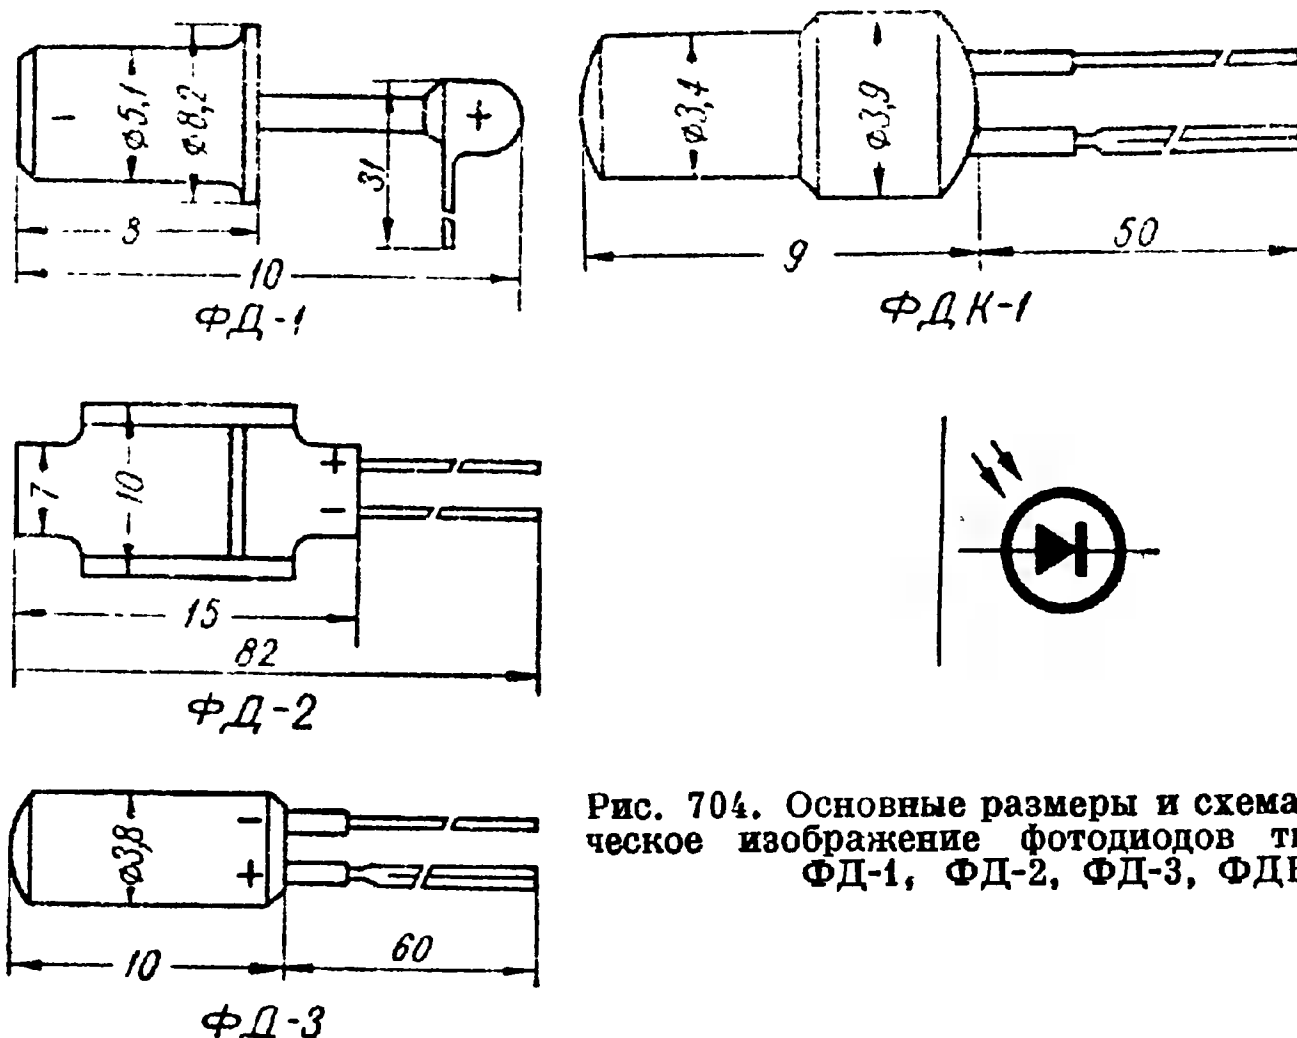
Основные размеры и схематическое изображение фотодиодов типа ФД-1, ФД-2, ФД-3, ФДК-1.
